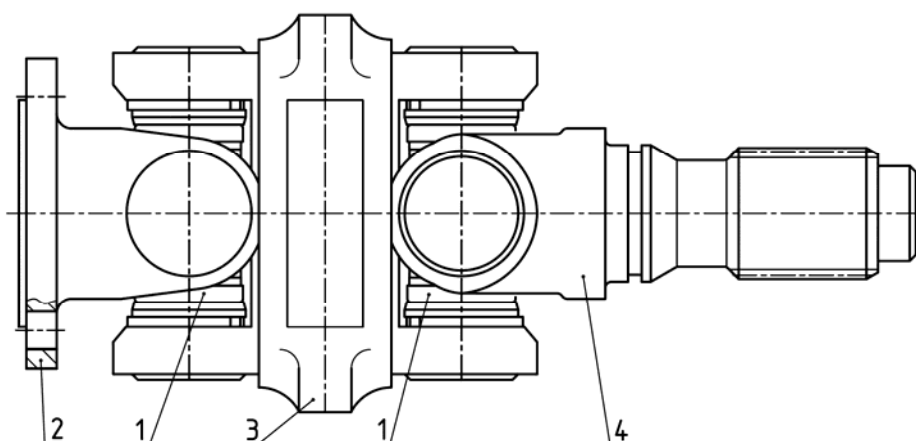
Сдвоенный шарнир двигателя DEUTZ.
